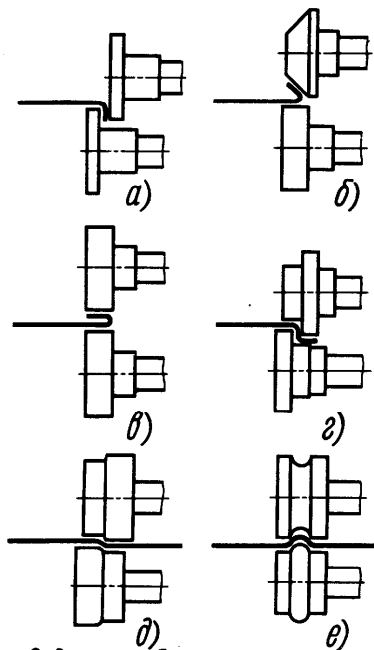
Схемы гибки на зигмашинах: а...г — гибка кромок; д, е — рельефная формовка
